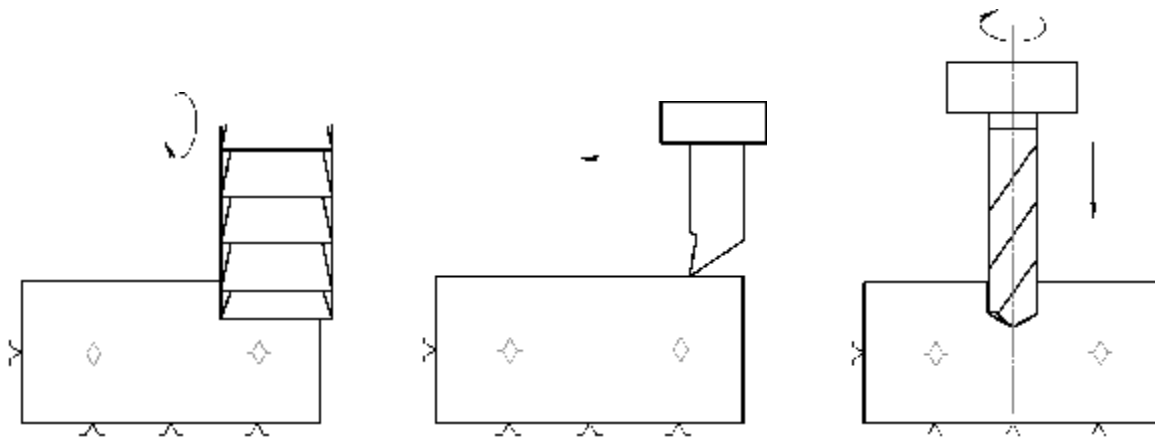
Типові схеми обробки призматичних деталей та схеми їх базування
